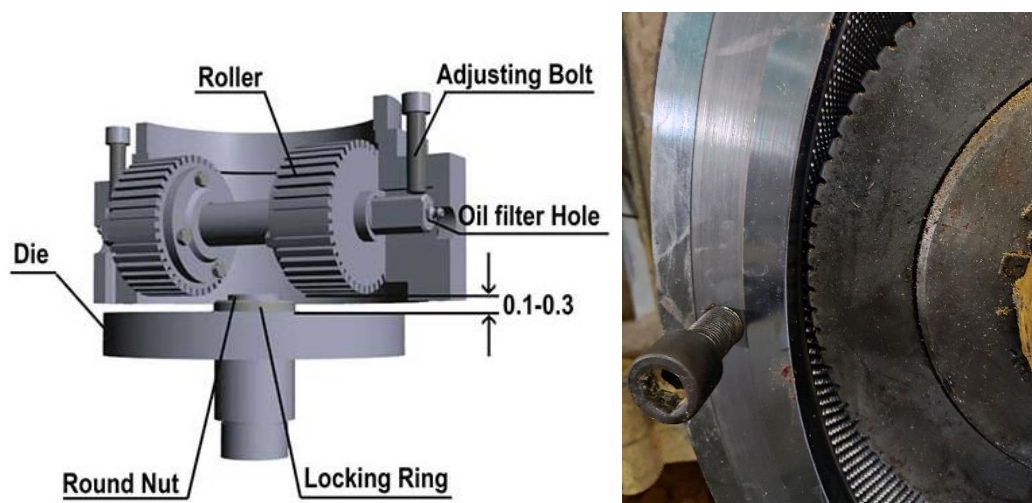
Suku Cadang *Ring Die Pellet Mill
